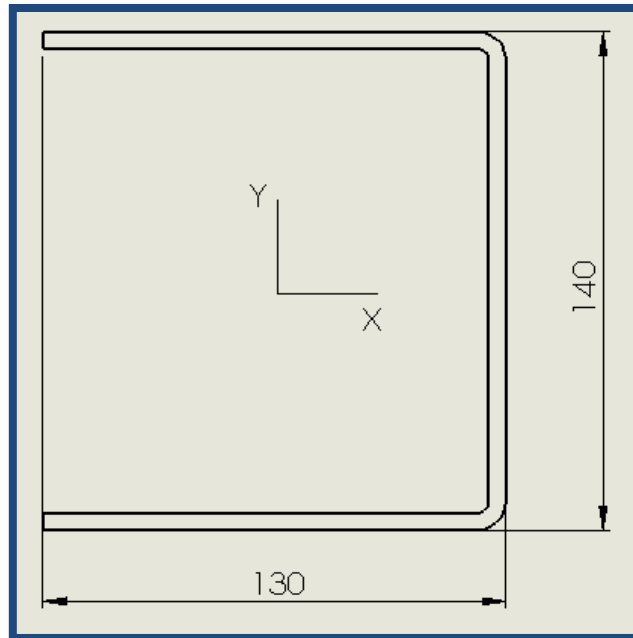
Sección del plegado con medidas generales.
